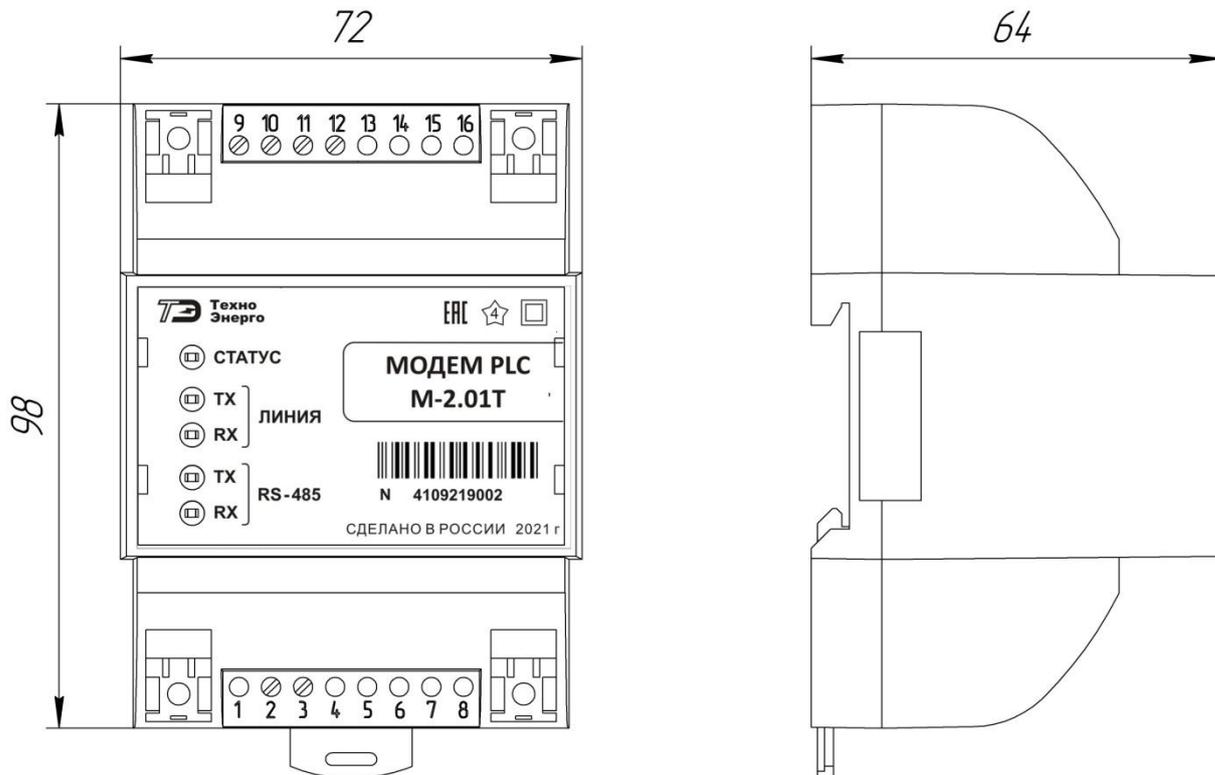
Внешний вид и габаритные размеры модема PLC M-2.01T
